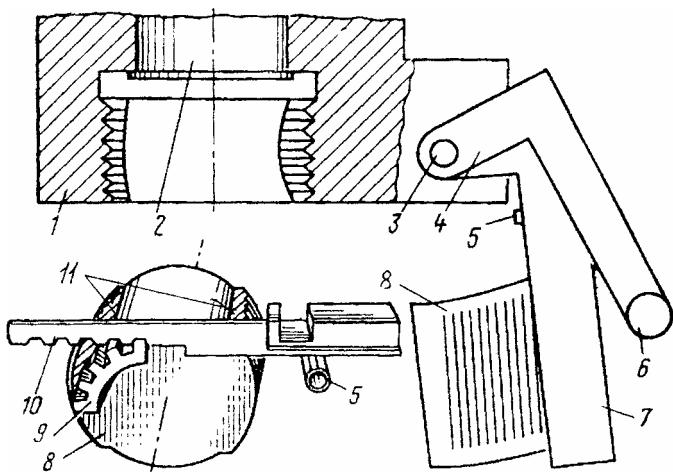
Схема поршневого затвора с приводом реечно-шестереночного типа.
